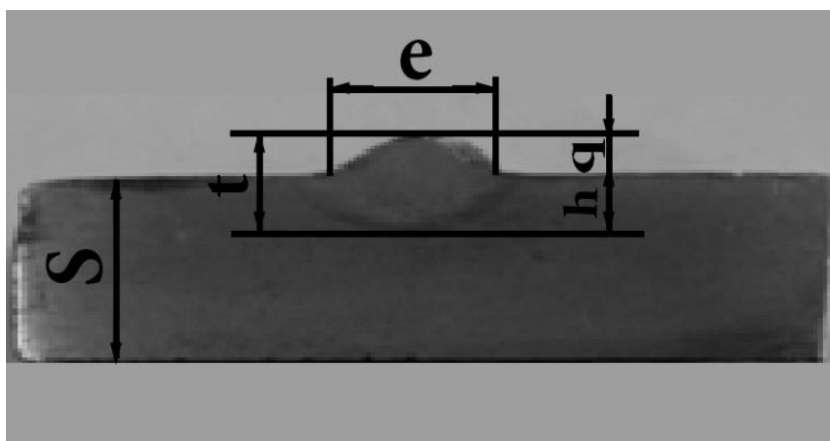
Основные геометрические параметры шва:  $S$  – толщина свариваемого металла;  $e$  – ширина сварного шва;  $q$  – выпуклость стыкового шва (высота усиления) – наибольшая высота (глубина) между поверхностью сварного шва и уровнем расположения поверхности сваренных деталей;  $h$  – глубина провара (глубина проплавления) – наибольшая глубина расплавления основного металла;  $t$  – толщина шва,  $t = q + h$ .
